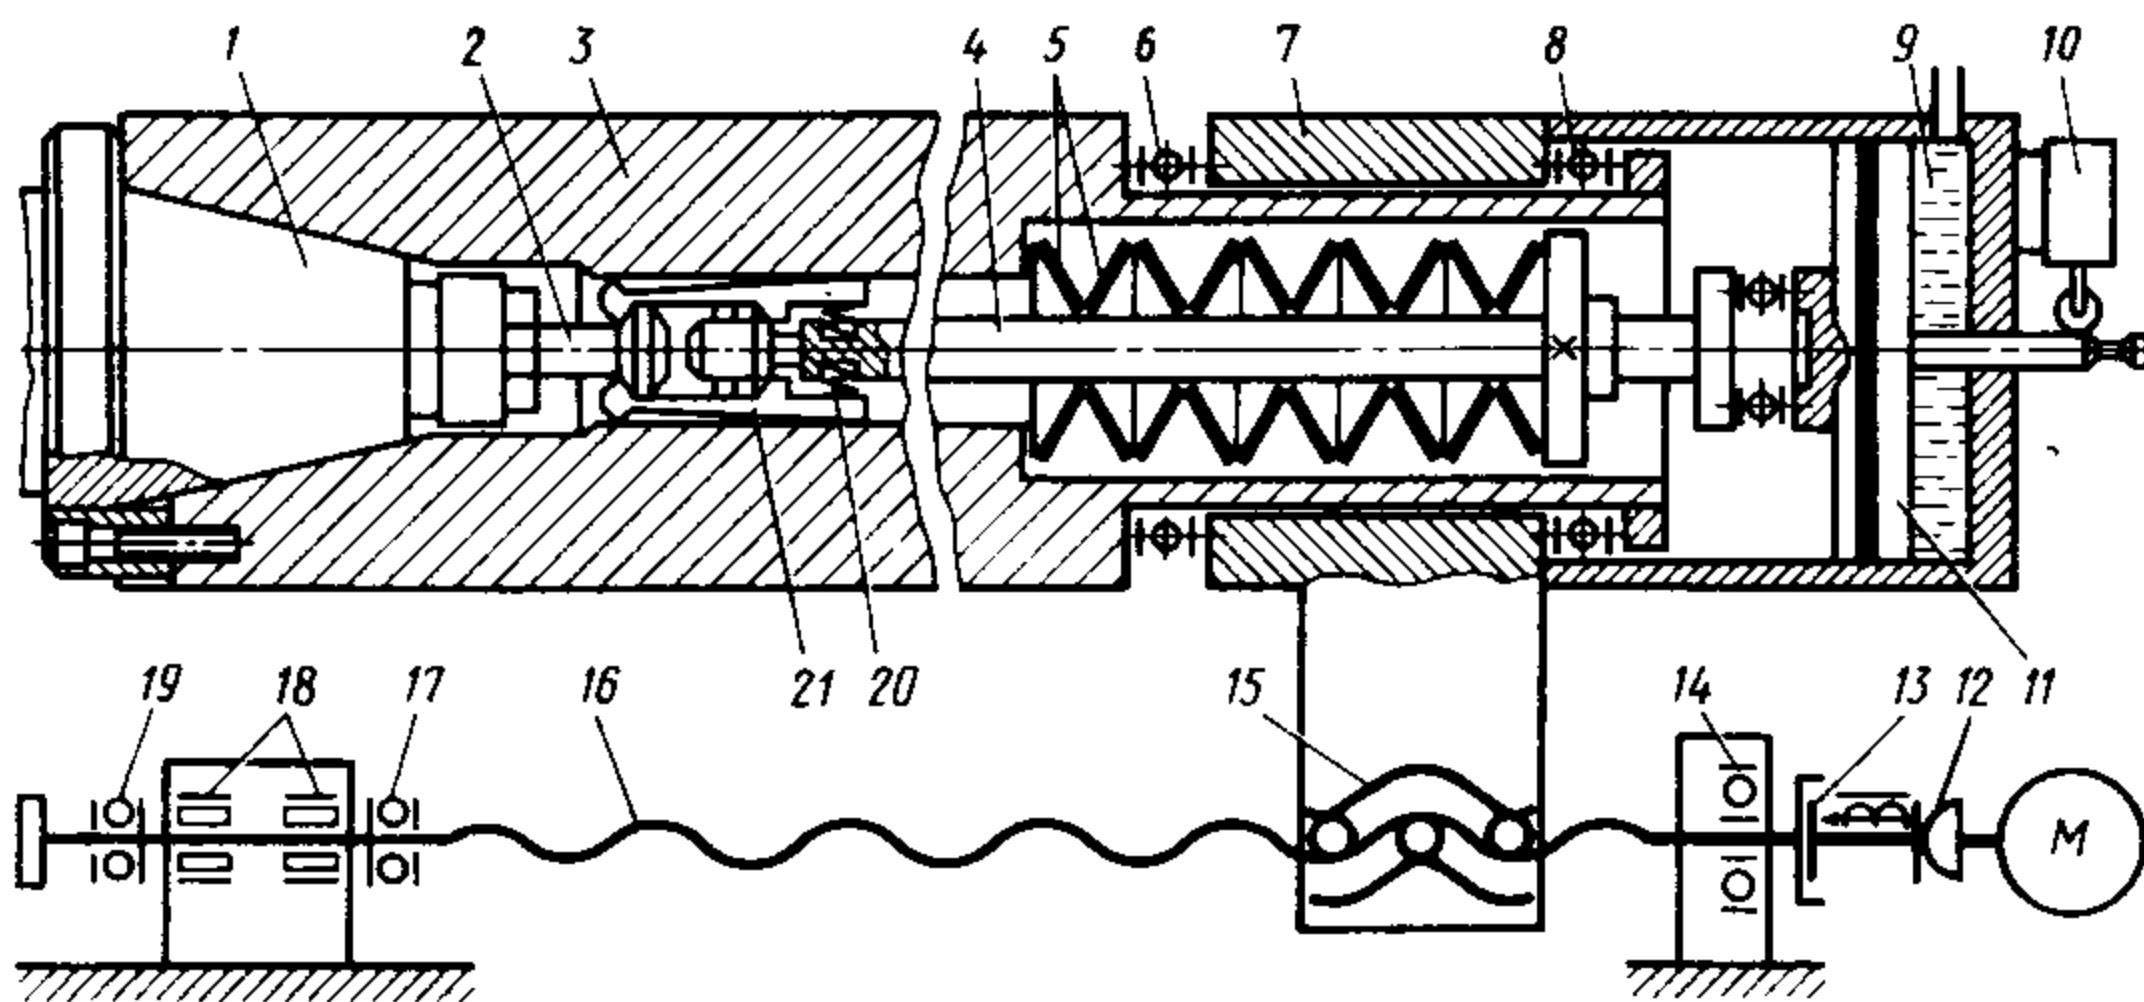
Схема привода осевой подачи шпинделя и закрепления инструментальных оправок на станке 2623ПМ4
